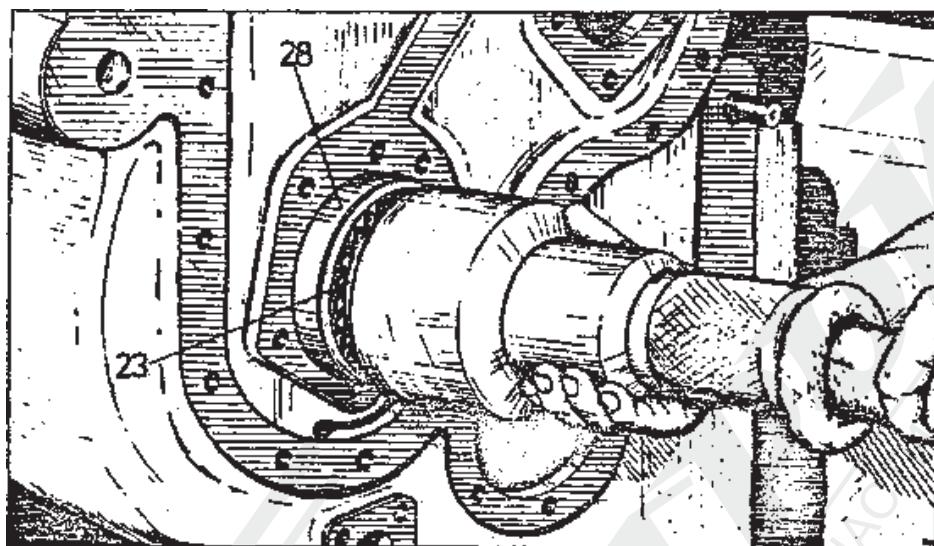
Вдавливание бочкообразного роликоподшипника 22217 /28/ на втулку гильзы 23 и в гнездо корпуса коробки скоростей.
